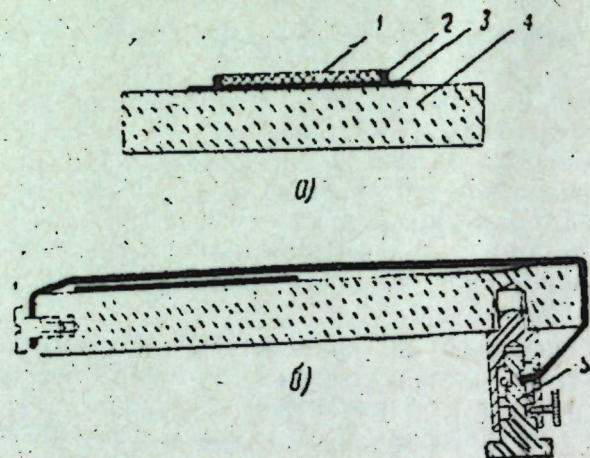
Схематическое изображение приспособления для изготовления поглотителя.
